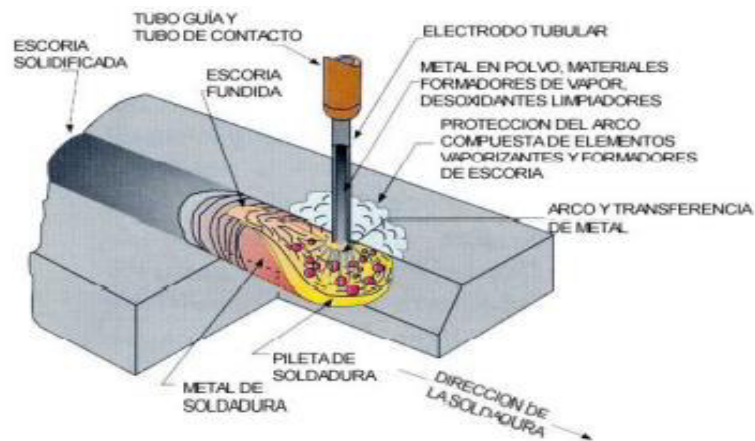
Soldadura por arco con núcleo de fundente protegido con gas.
